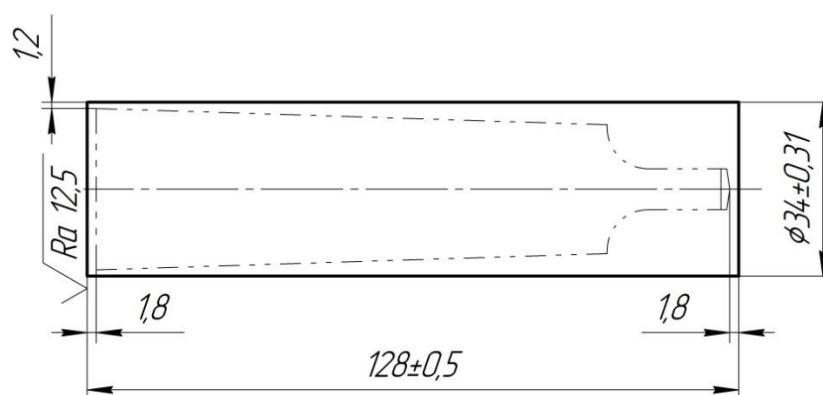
Эскиз заготовки хвостовой части зенкера
